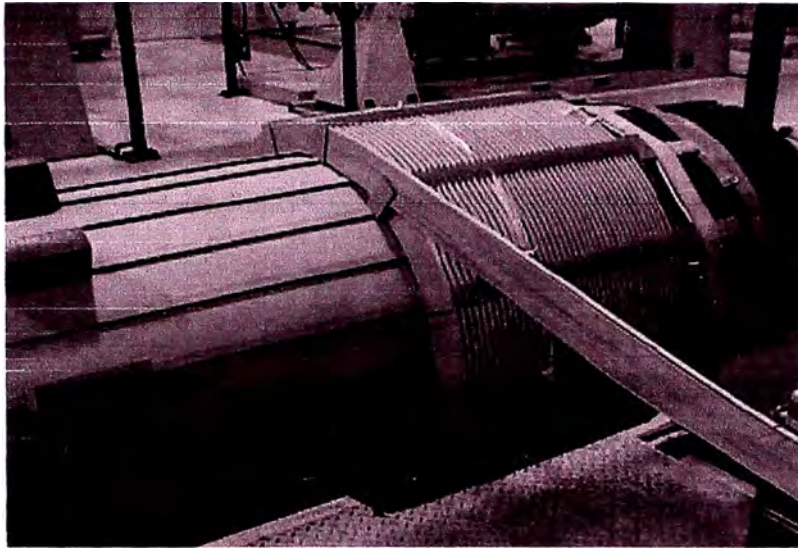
Bobinado tipo hélice, durante el bobinado
